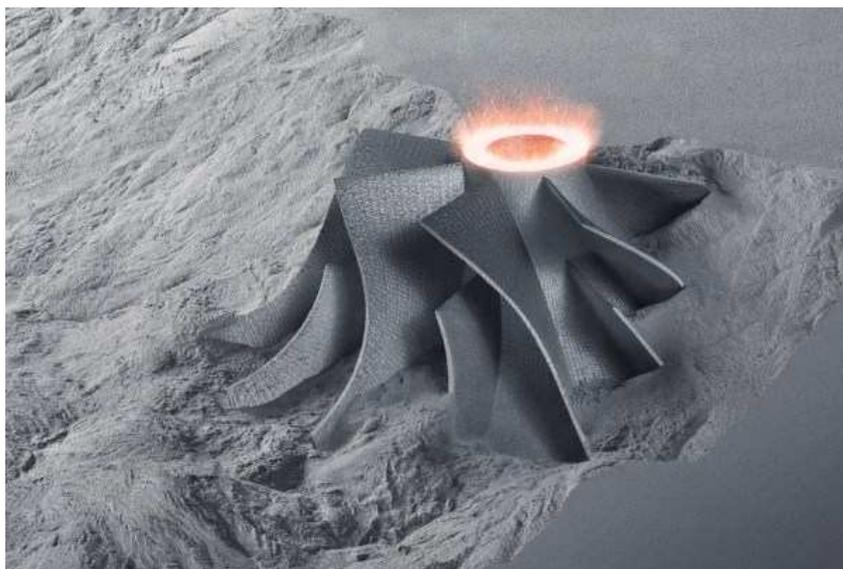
Impressão por Processo de "Laser Sintering". Fonte:
